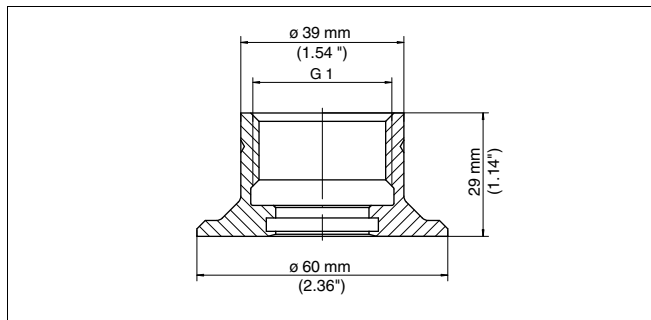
Размеры приварного штуцера G1 A по DIN 3852-X
